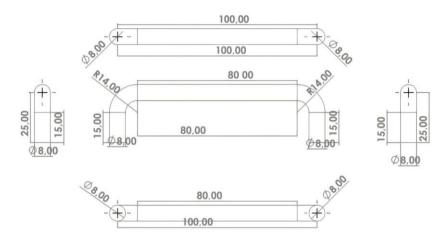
Mise en plan de la poignée sur SolidWorks.
